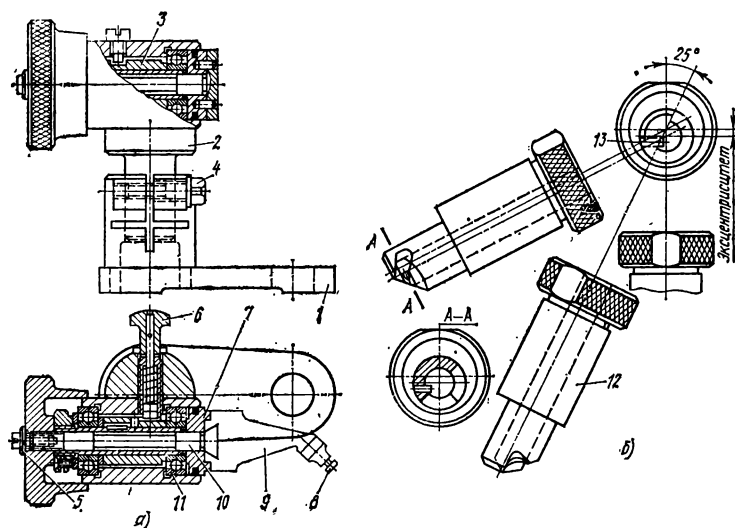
Приспособление для заточки сверл диаметром 2—10 мм:
